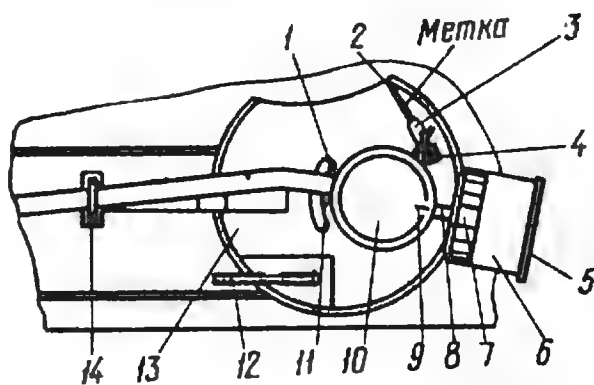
Устройство управления звукоснимателем: 1 — гайка регулировки положения звукоснимателя над грампластинкой, 2 — шток компенсатора, 3 — груз компенсатора, 4 — компенсатор скатывающей силы, 5 — зубчатый торец противовеса, 6 — противовес, 7 — колпачок, 8 — ось, 9 — риска, 10 — колпак, 11 — винт регулировки микролифта, 12 — рычаг микролифта, 13 — неподвижное основание, 14 — стойка
